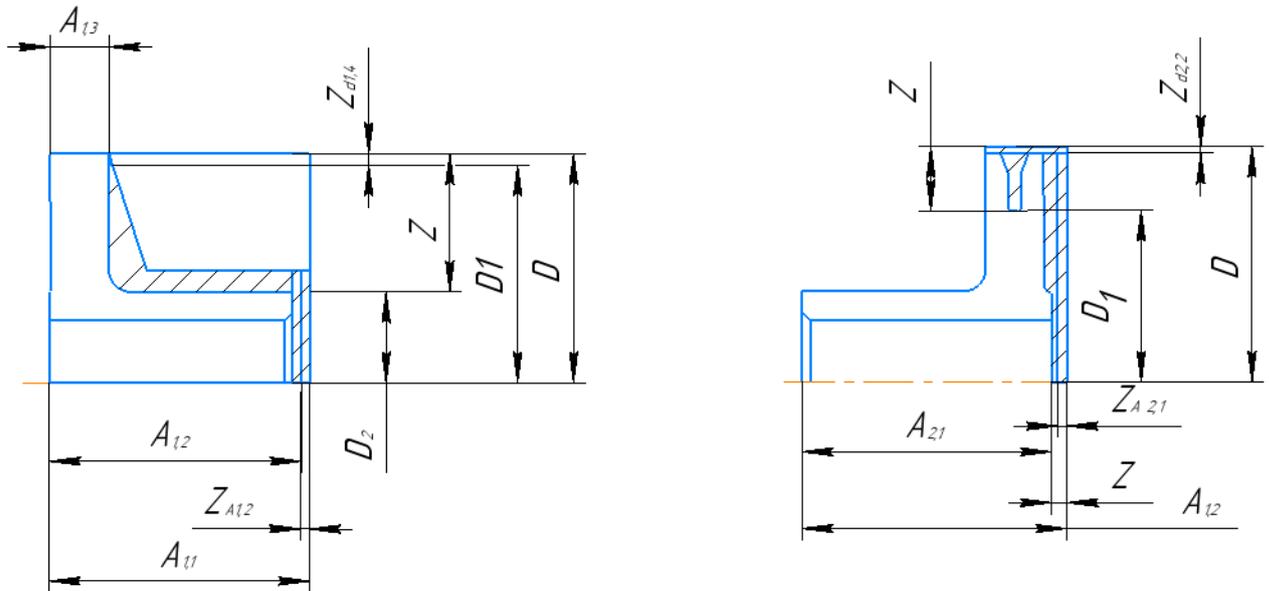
Размерная схема токарной операции с ЧПУ
